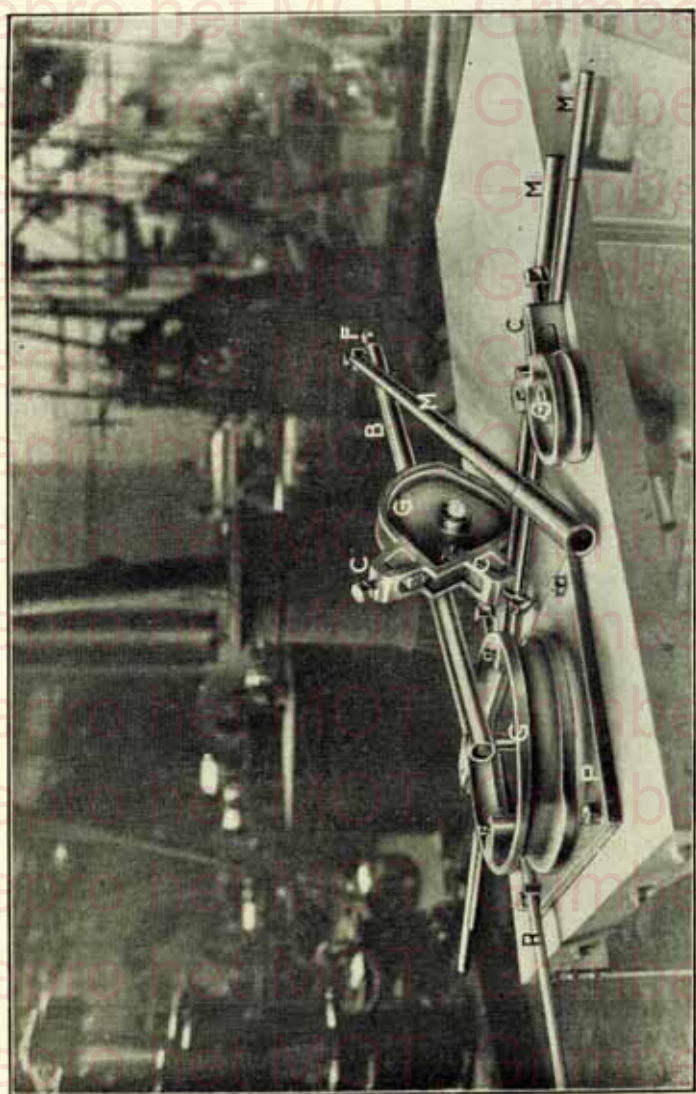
Machine à cintrer "Monobloc Breveté" sur table-établi.
